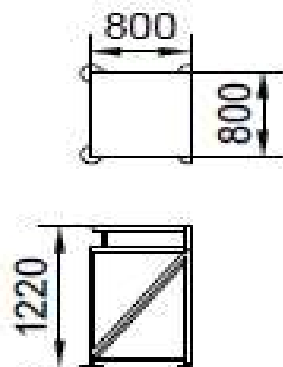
Габаритные размеры. Перегрузочный стол.
